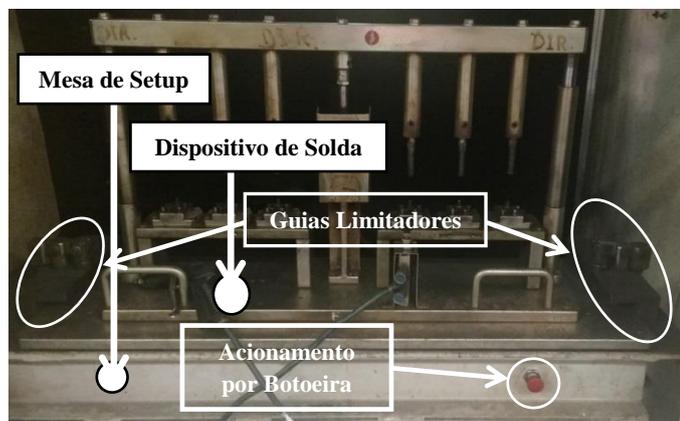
Nova Mesa de Setup com dispositivo de solda fixado.
